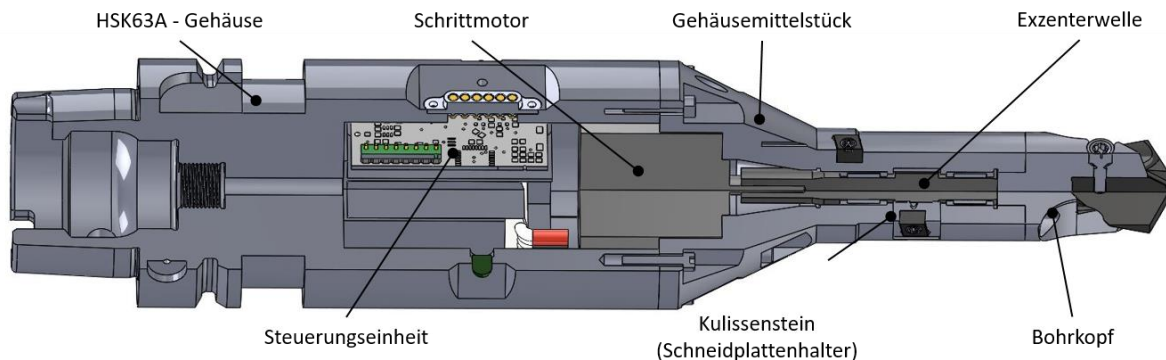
Elektromechanisch arbeitendes Demonstratorwerkzeug
